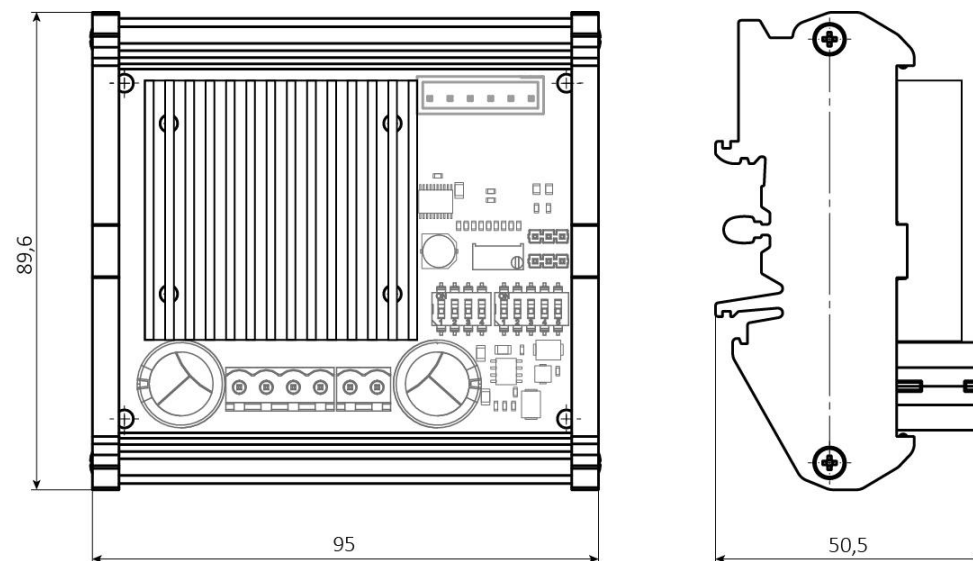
Габаритные и присоединительные размеры драйвера шагового двигателя SMD-8.0 с DIN-фиксатором.
